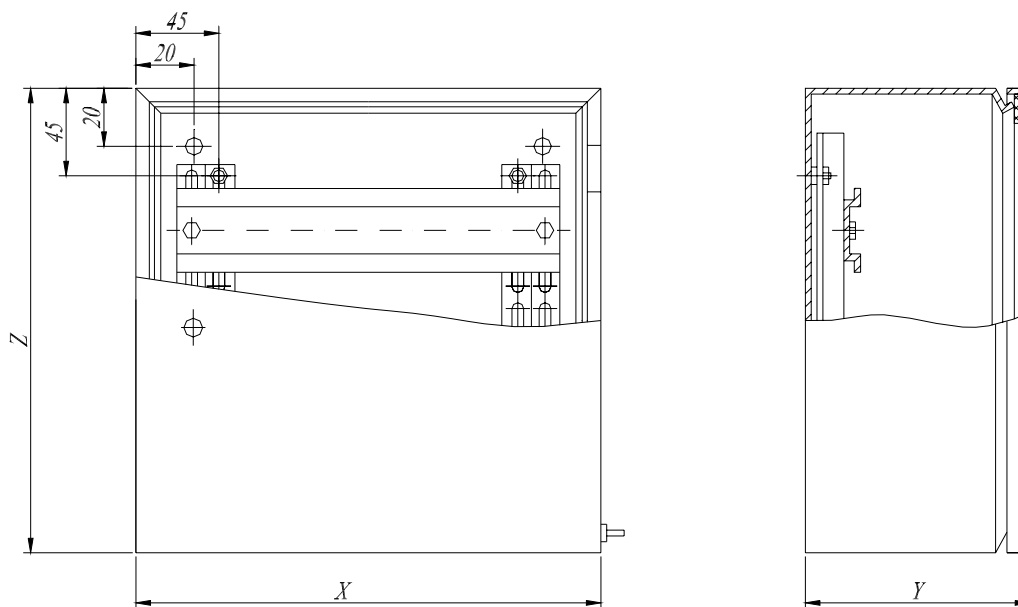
Общий вид корпусов (34X - навесной, 24X - напольный).
